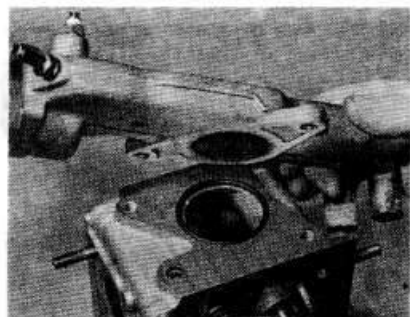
Снятие корпуса термостата с головки блока цилиндров — двигателя 2,0 л с одним распредвалом
